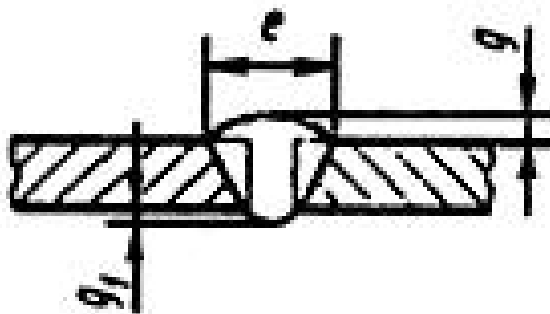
Конструктивные элементы сварного шва С2
